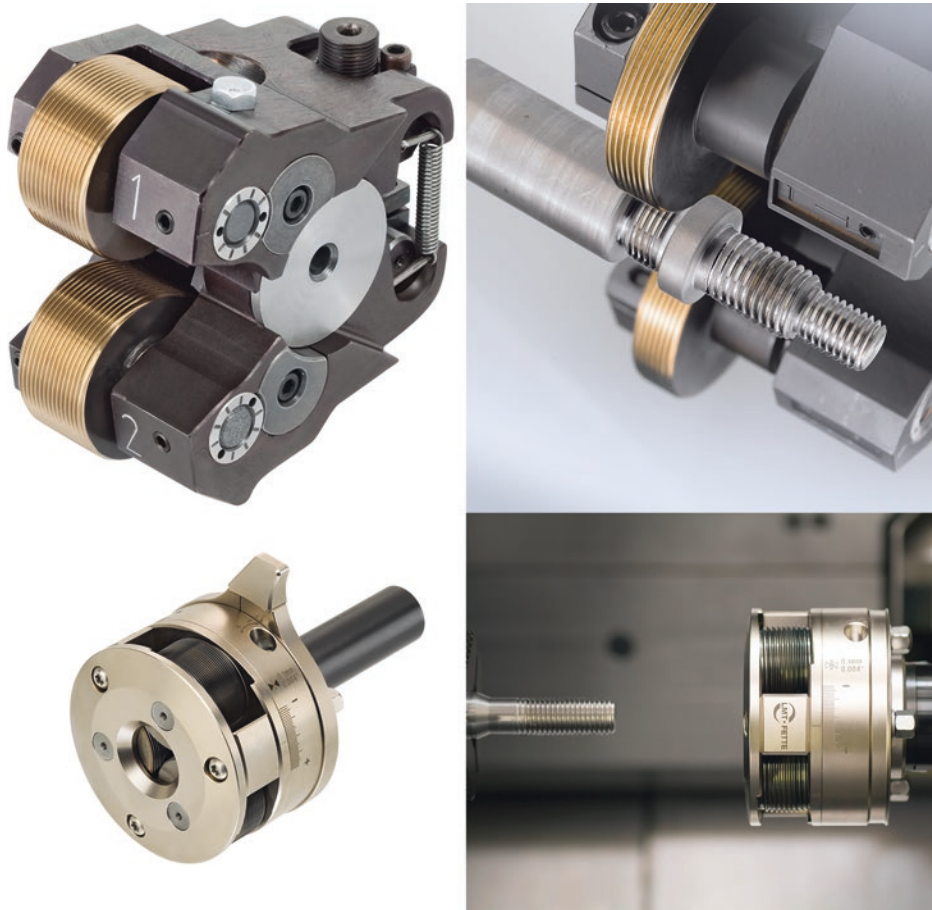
Rollköpfe und Prozessbilder für das tangentielle (oben) und axiale (unten) Gewinderollen [Lmt17]
